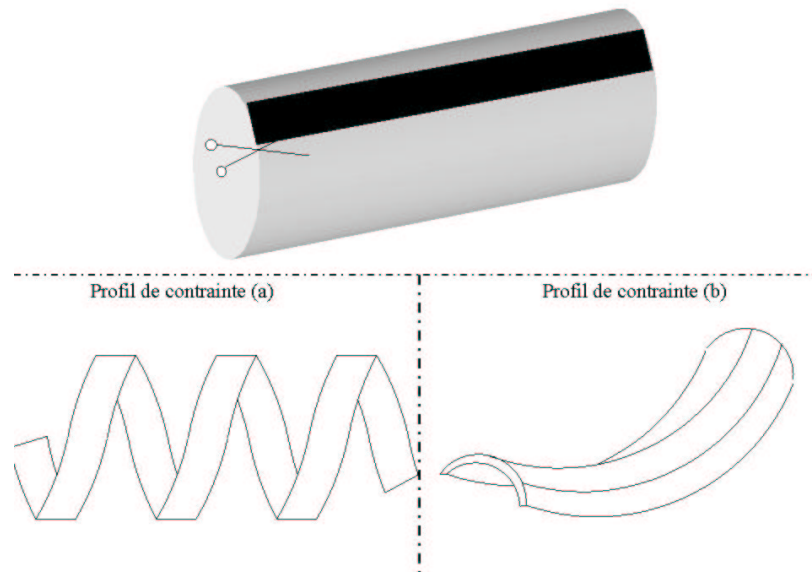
découpe d'une bande parallèlement a la génératrice
